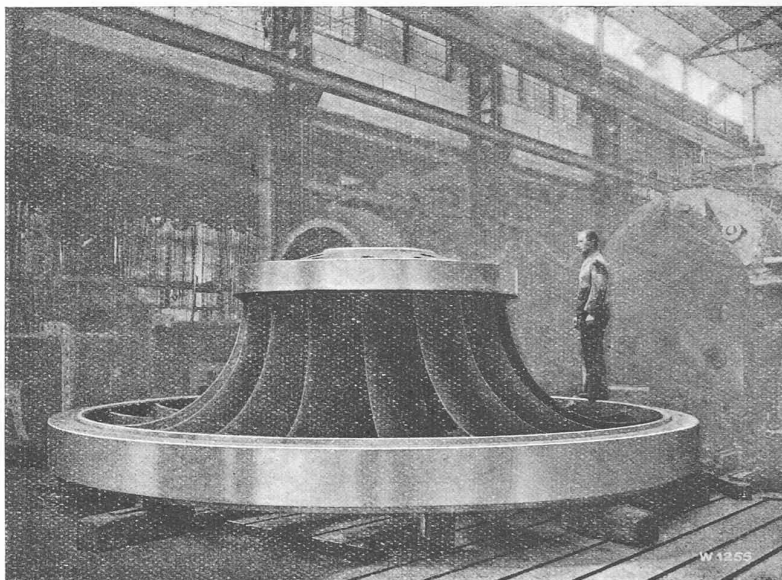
Vue de la roue motrice des turbines Escher-Wyss de l'usine de Chancy-Pougny.
